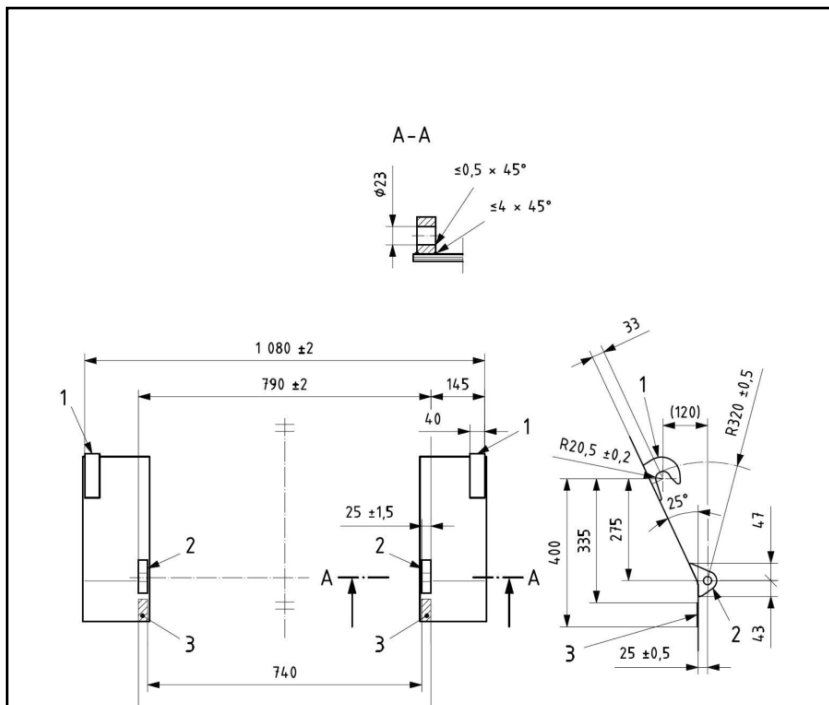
Габаритные размеры для агрегатирования еврорамки фронтального погрузчика
